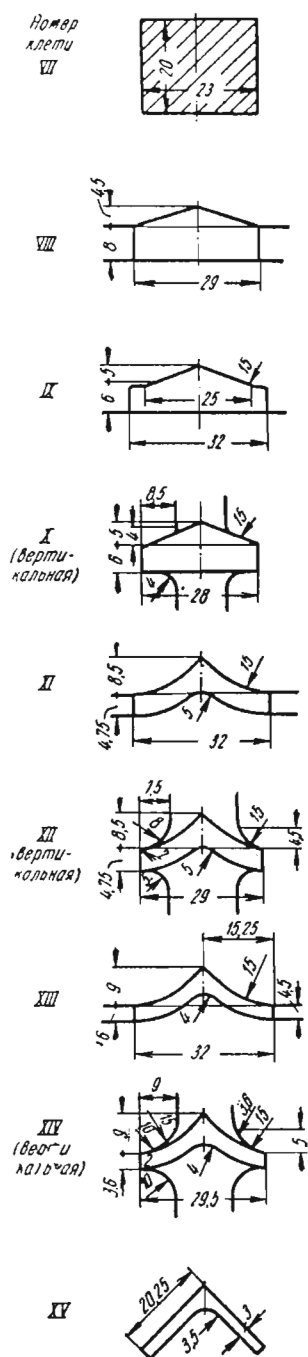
Схема прокатки и калибровки угловой стали с применением открытых калибров (последние девять клетей или проходов мелкосортного стана 250)
